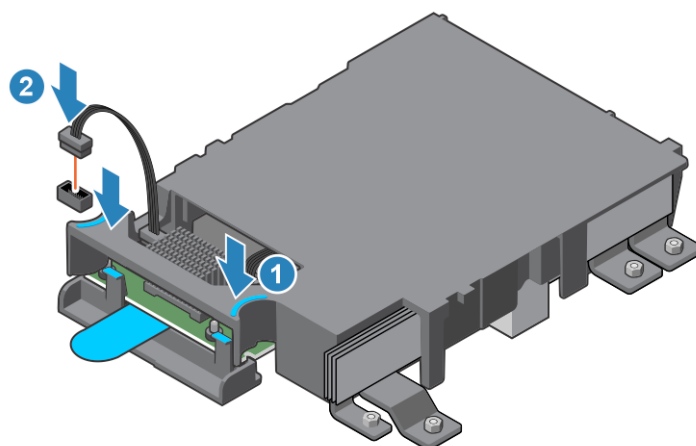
Instalación de la cubierta y conexión del cable del Módulo de batería de reserva interna
